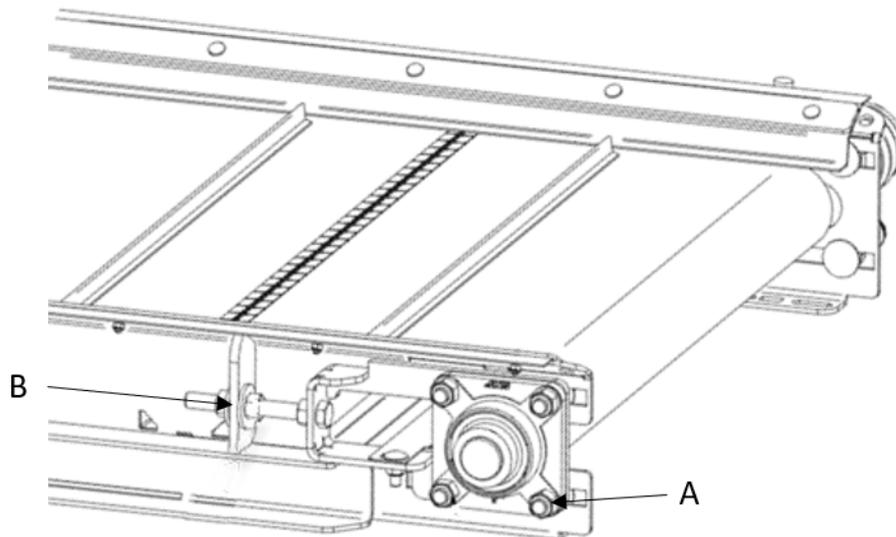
Réglage de la tension de la courroie du convoyeur horizontal ou incliné
